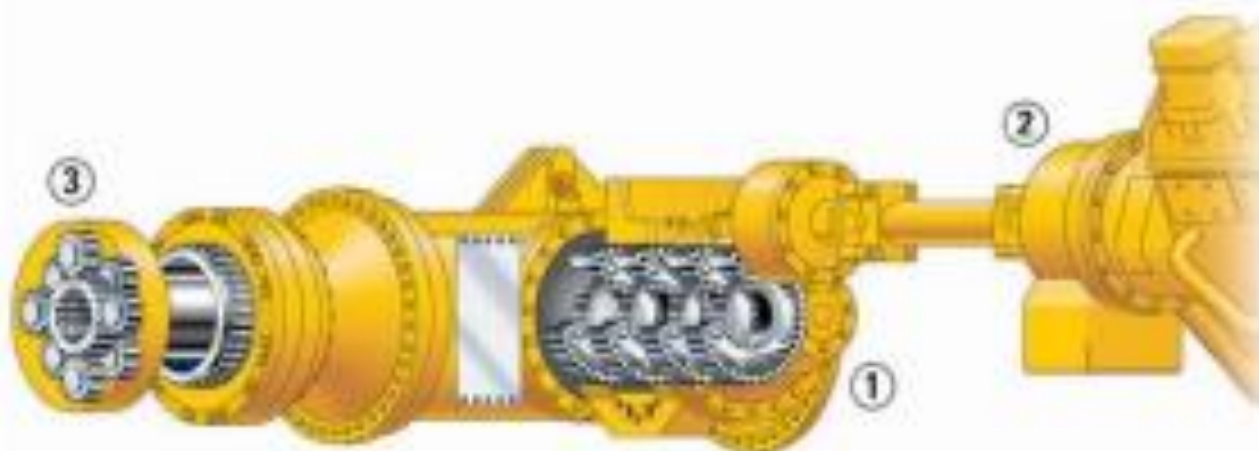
Силова передача самоскиду Caterpillar 797F: 1 – коробка передач; 2 – гідротрансформатор з муфтою блокування; 3 – бортовий редуктор
